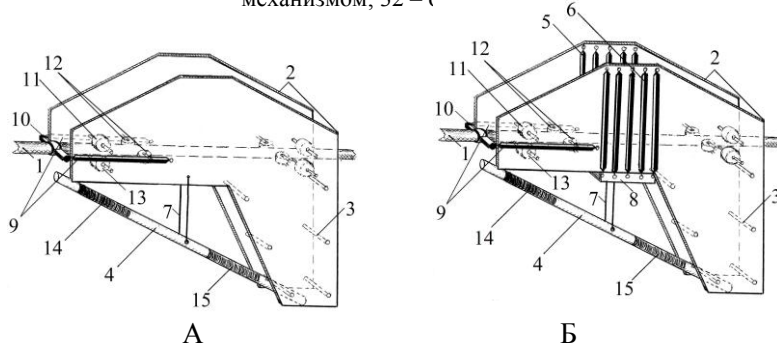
Тренажер № 2 (А – для обучения прыжку на прямом шесте; Б – для обучения прыжку на эластичном шесте): 1 – гимнастическая перекладина; 2 – корпус тренажера; 3 – соединительный болт; 4 – шест; 5, 6 – блоки «внутренних» и «внешних» вертикальных пружин; 7 – соединительная тяга; 8 – соединительная деталь; 9 – горизонтальные пружины; 10 – фиксирующая клемма; 11 – опорный ролик; 12, 13 – прижимные ролики; 14, 15 – места захвата
